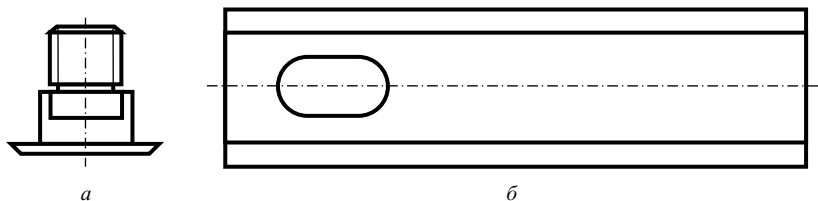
Детали ротора: *а* – ось ножа; *б* – нож
